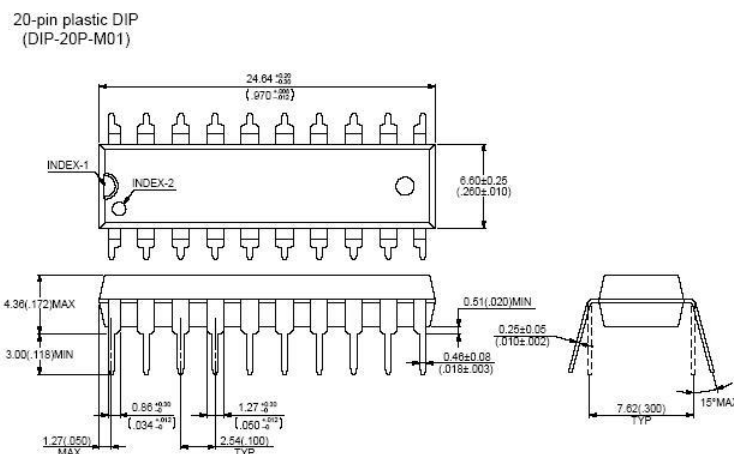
Габаритні розміри мікросхеми AT90S2313
